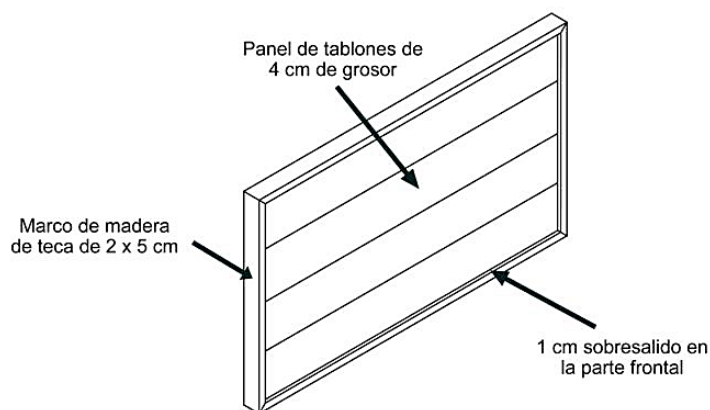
Detalle de los ensambles para la construcción de los paneles de madera
